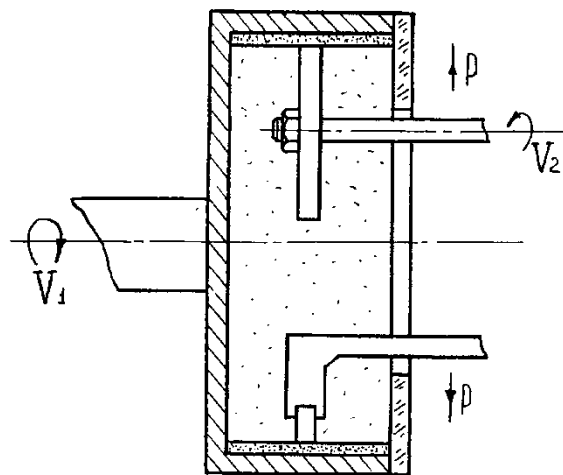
Обработка шлифовальным слоем неподвижной и вращающейся деталей
